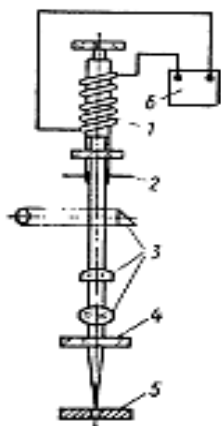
Схема установки для лазерної обробки матеріалів: 1 – оптичний квантовий генератор; 2 – діафрагма; 3 – оптичний мікроскоп для наведення променя; 4 – захисне скло; 5 – оброблювана заготовка; 6 – блок живлення
